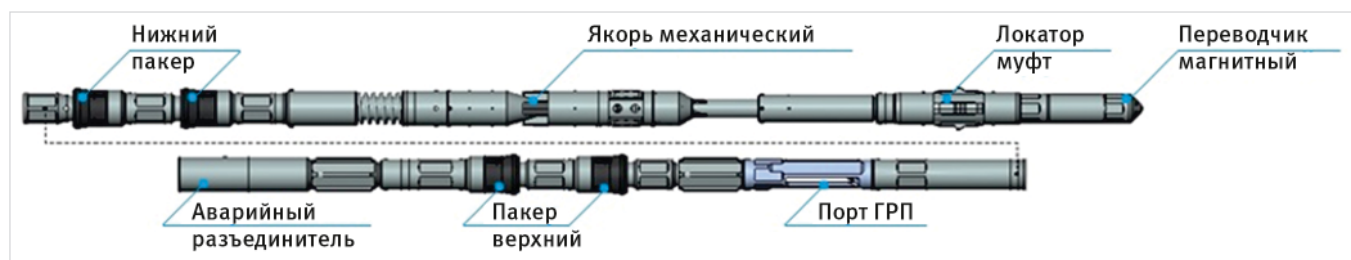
Компоновка со сдвоенными манжетными пакерами
